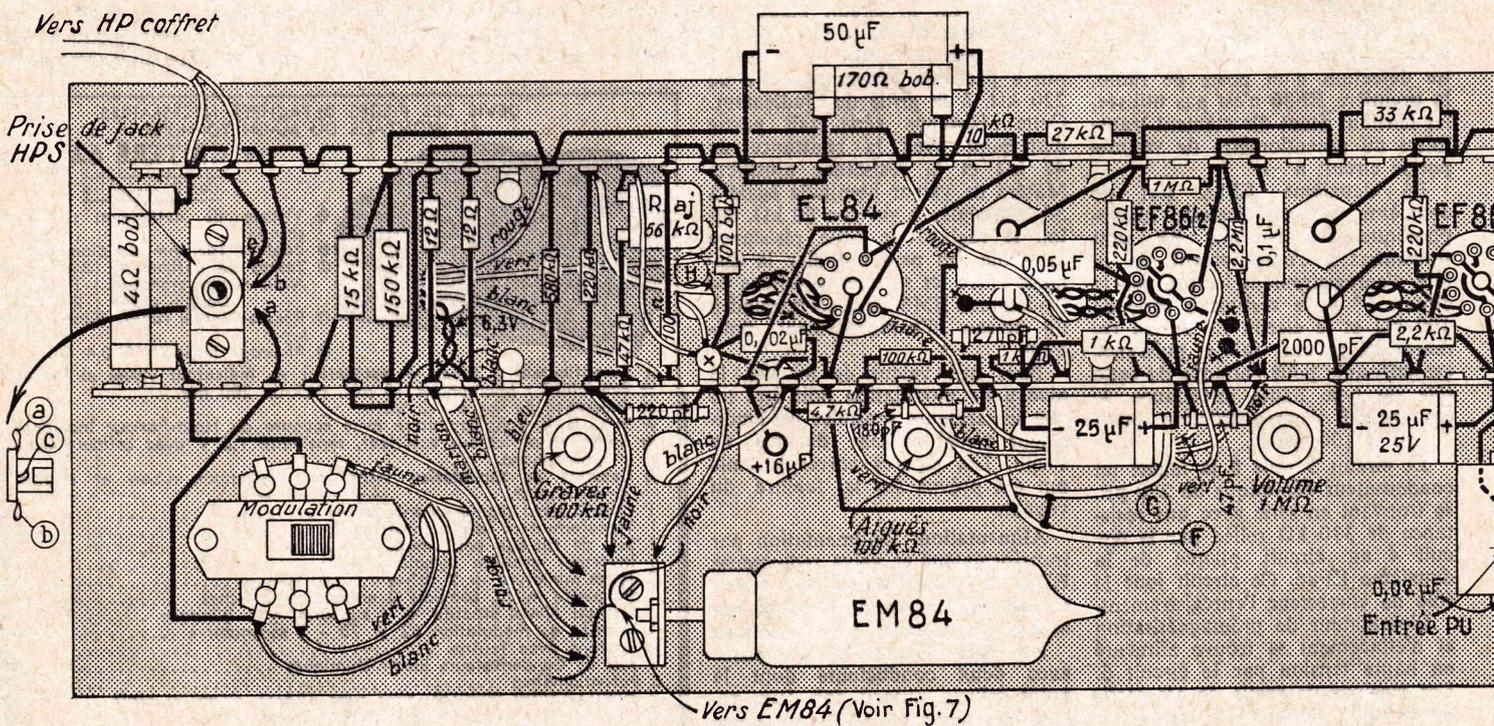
Câblage de la partie inférieure du châssis principal.
